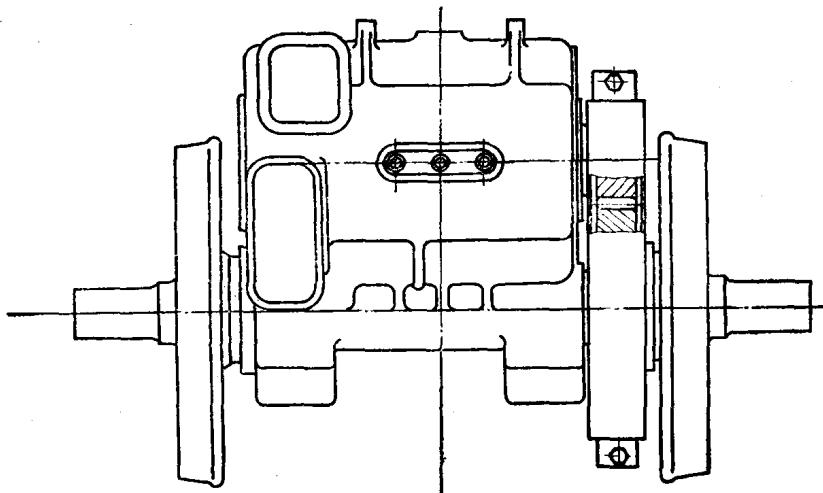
7 东风型内燃机车单边刚性齿轮传动装置
